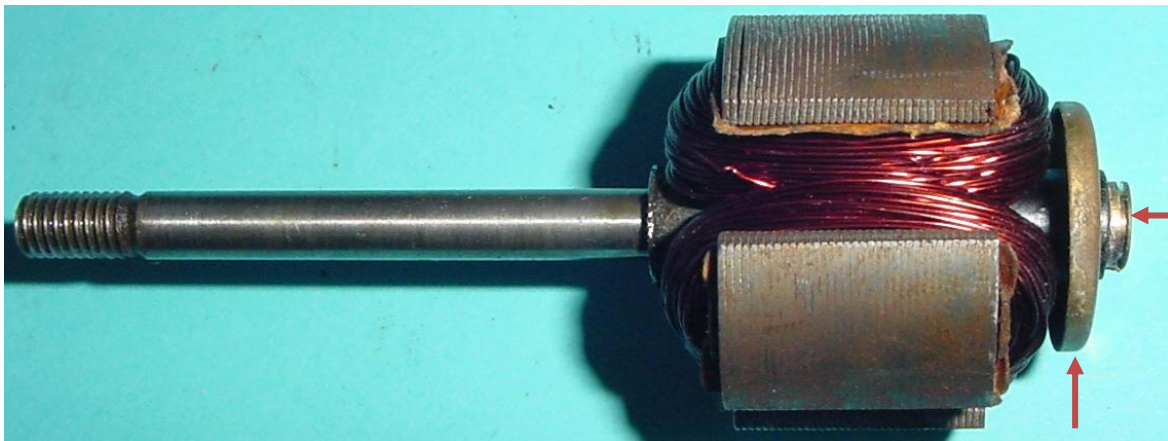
Sternanker mit zwei Schleifkontakten: Blechpaketlänge: 18 mm, Durchmesser: 29 mm,
